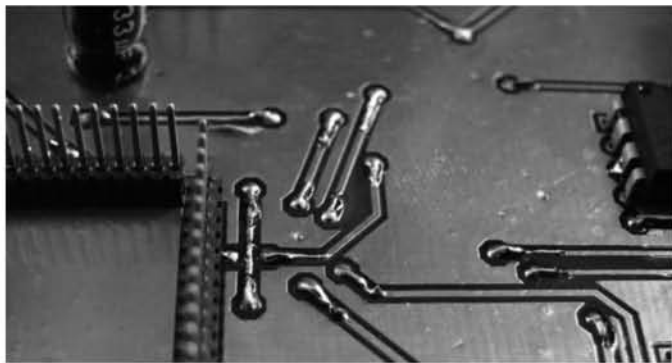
Puentes metálicos y soldaduras.
